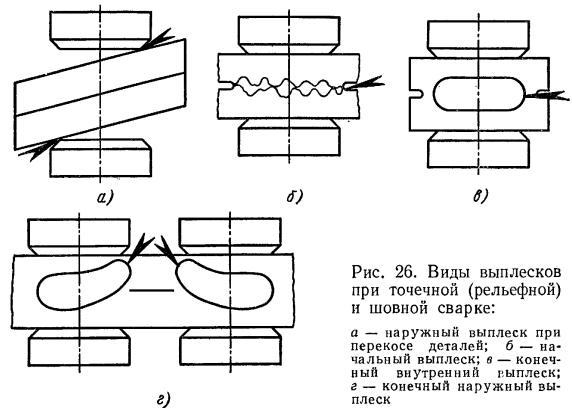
Виды выплесков при точечной (рельефной) и шовной сварке:
